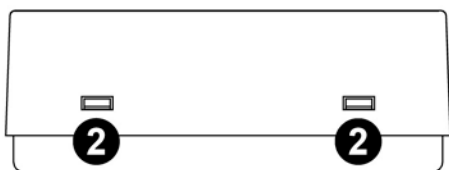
Расположение пластиковых зубцов — крепежей крышки прибора
